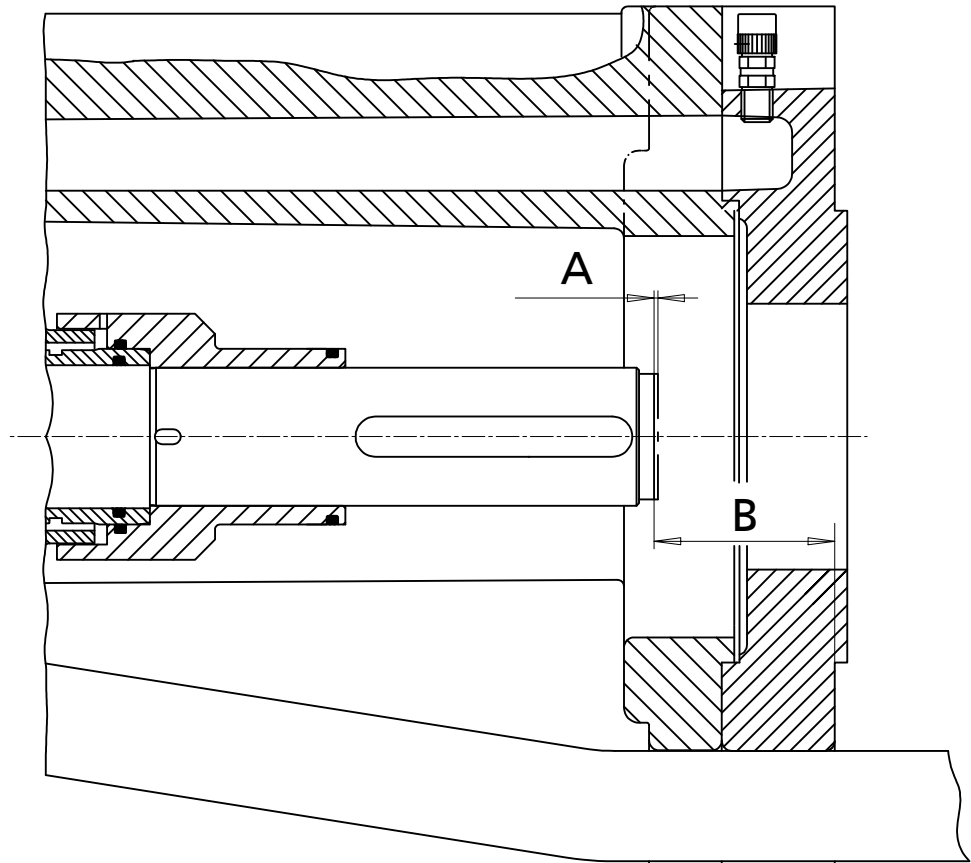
Установочные размеры для двигателей V, X, Z, E
